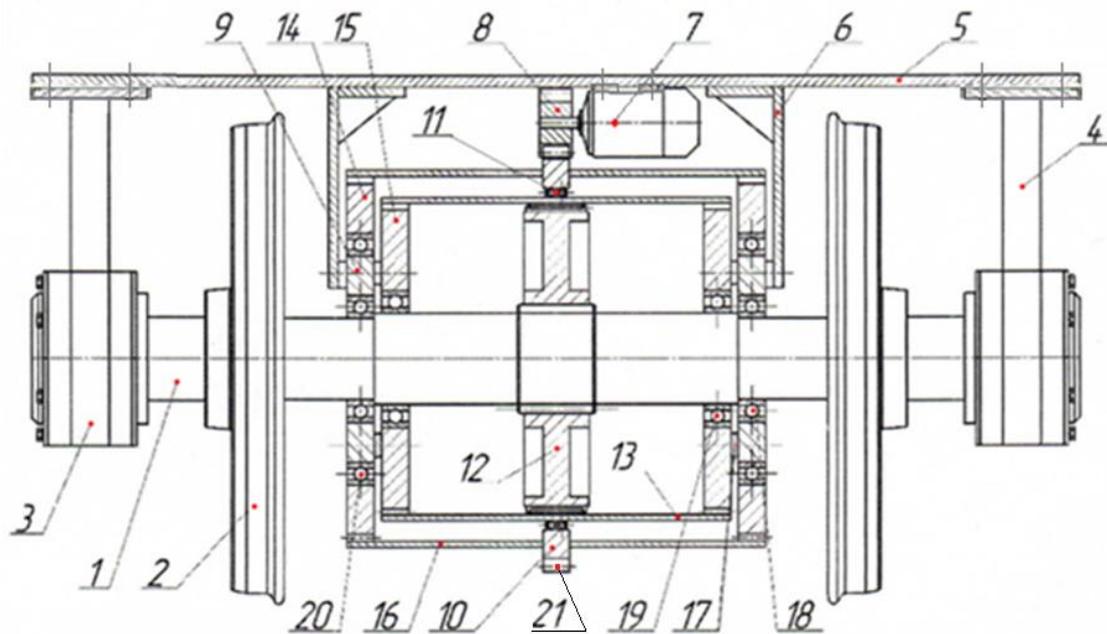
Схема рациональной конструкции привода передвижения металлургической машины
